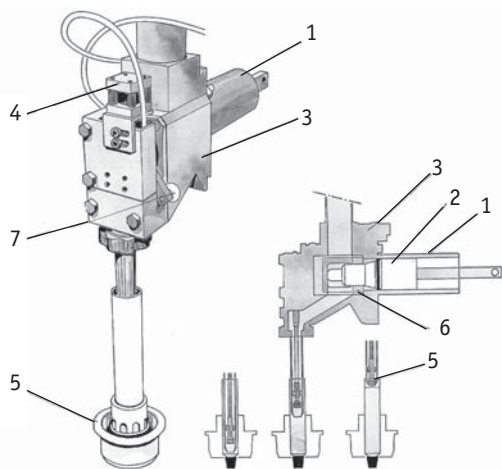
Поршневий дозувальний пристрій пакувальної машини NORDENMATIC 400 (Швеція), загальний вигляд (а) і стадії фасування продукції у туби (б): 1 – мірний циліндр; 2 – поршень; 3 – корпус дозатора; 4 – пневмопривід штока витискного клапана; 5 – витискний клапан; 6 – впускний кран; 7 – ролик із важелем для повороту крана
